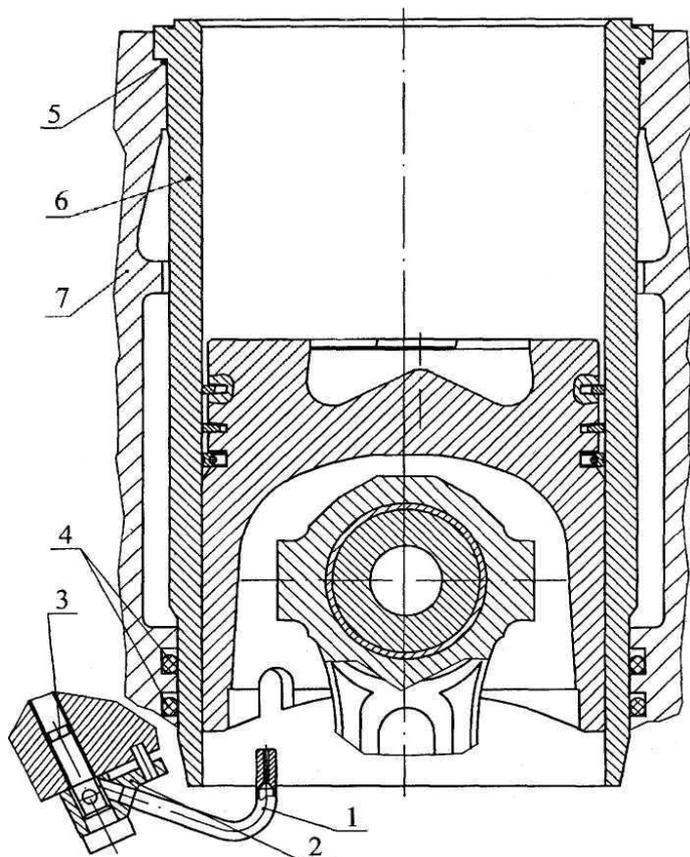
Установка гильзы цилиндра и уплотнительных колец: 1 - трубка форсунки; 2 - корпус форсунки охлаждения поршня; 3 - корпус клапана; 4 - кольцо уплотнительное гильзы нижнее; 5 - кольцо уплотнительное верхнее; 6 - гильза цилиндра; 7 - блок цилиндров
